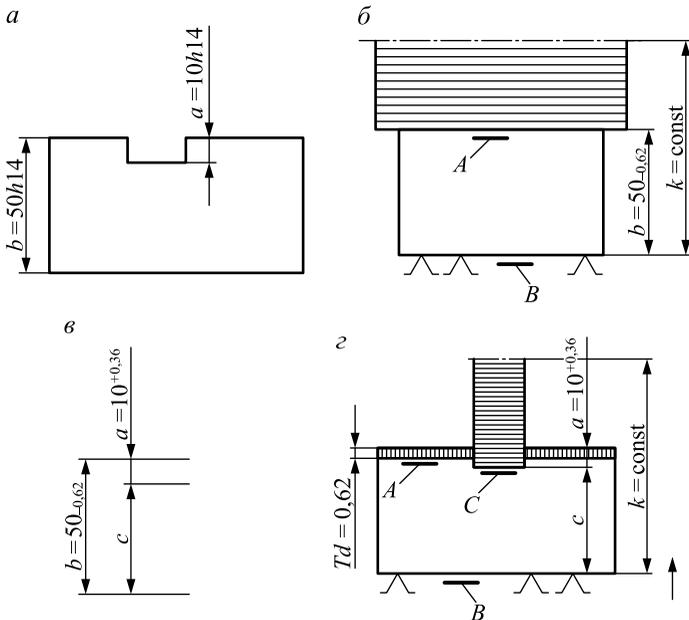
Фрезерование паза от опорной технологической базы, не совпадающей с конструкторской (а–з)
